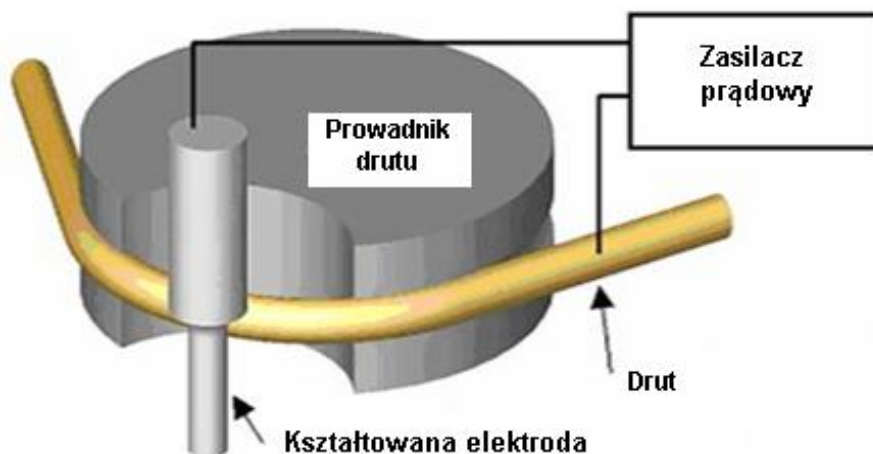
Schemat kształtowania elektrody roboczej z wykorzystaniem ruchu obrotowego i planetarnego [53, 93].
